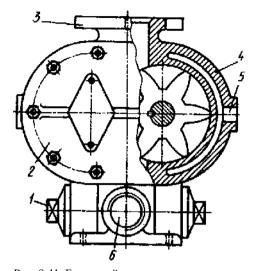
Битумный насос низкого давления: 1 – заглушка; 2 – крышка насоса; 3 – верхний патрубок; 4 – корпус насоса; 5 – подвод пара в паровую рубашку; 6 – отверстие выдачи битума
